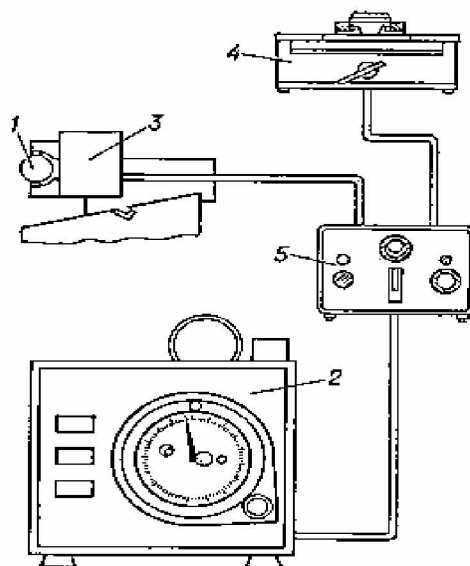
Схема прибора активного контроля для сопряженного шлифования: 1 — обрабатываемая деталь; 2 — отсчётно-командное устройство; 3 — скоба для измерения диаметра вала в процессе обработки; 4 — измерительное устройство для определения диаметра отверстия, под которое обрабатывается вал; 5 — переключатель для подключения в отсчётно-командное устройство скобы (3) и измерительного устройства или совместного их включения.
